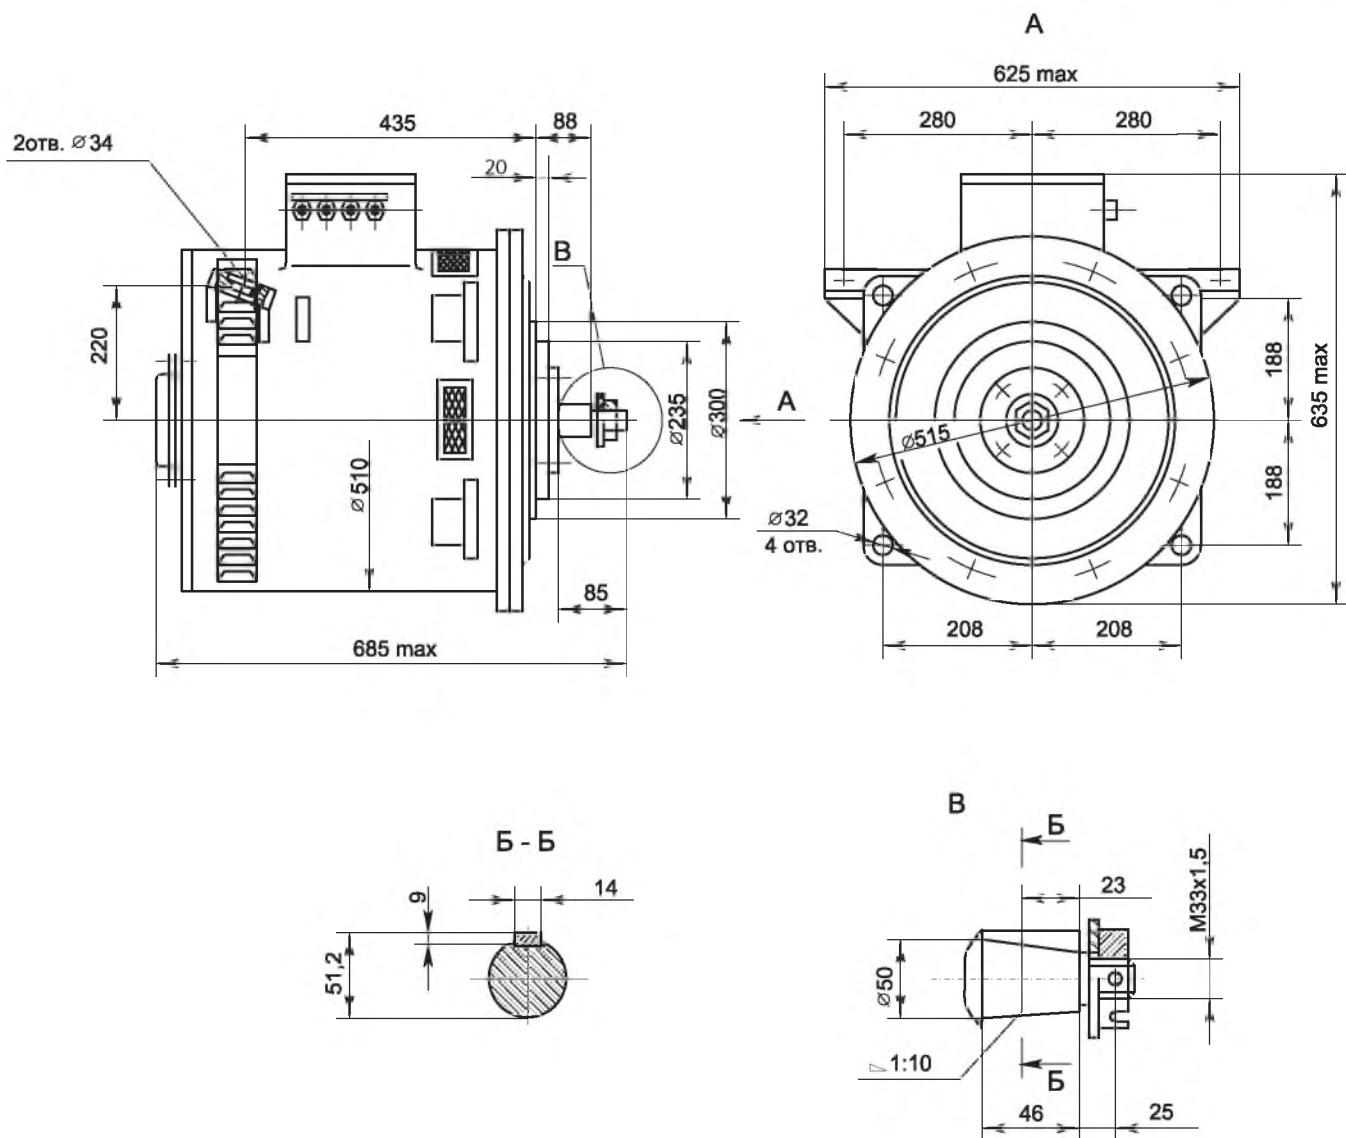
Габаритные и установочные размеры электродвигателя ДТН-34/25М
